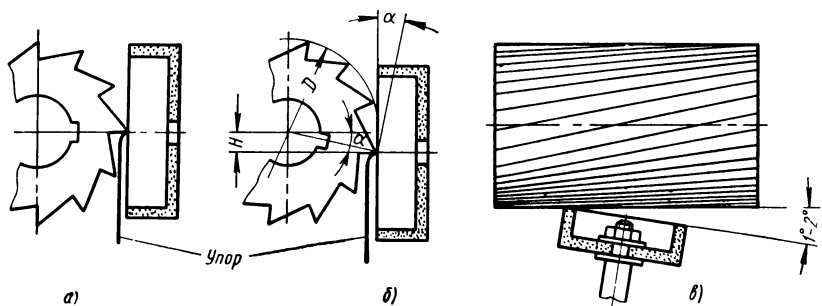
Схема заточки задней поверхности цилиндрических фрез с остроконечными зубьями
